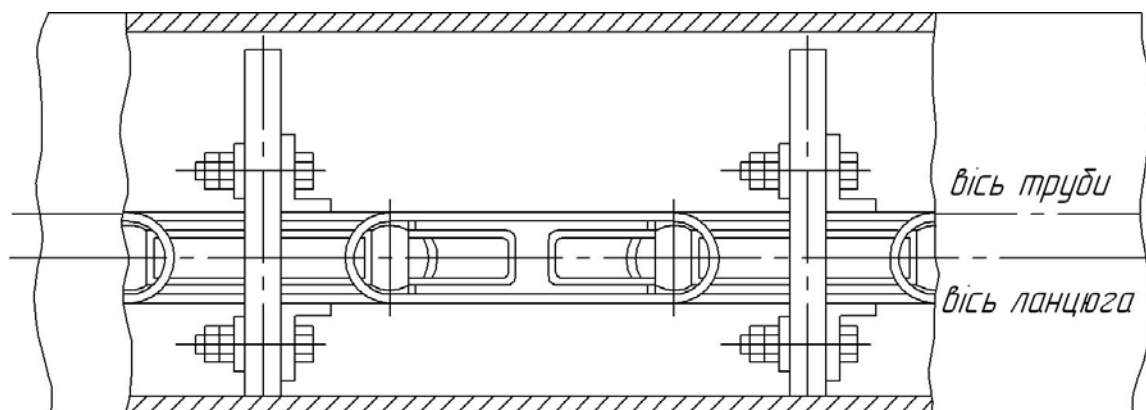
Схема робочих елементів трубного скребкового конвеєра
